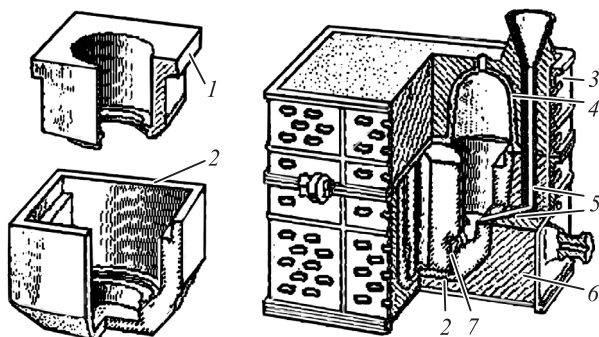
Технология ручного изготовления формы с применением оболочкового стержня: 1 – отливка; 2 – оболочковая вставка из жидкостекольной смеси; 3 – верхняя опока; 4 – облицовочный слой; 5 – литниковые огнеупорные трубки; 6 – нижняя полуформа; 7 – оболочковый стержень
